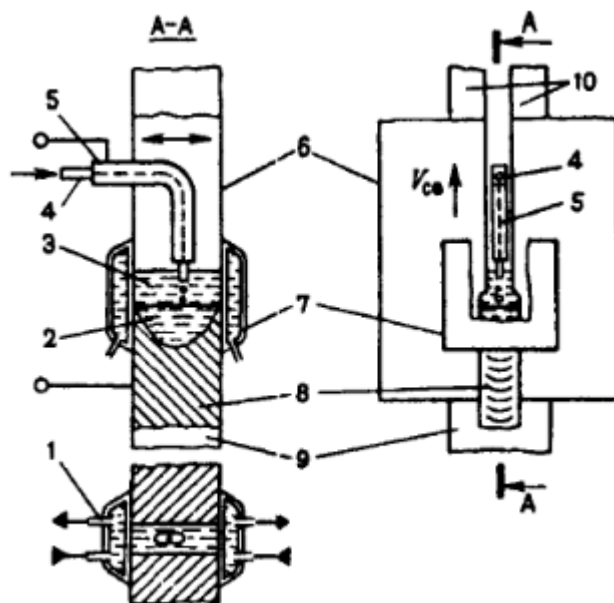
Схема процесса электрошлаковой сварки
